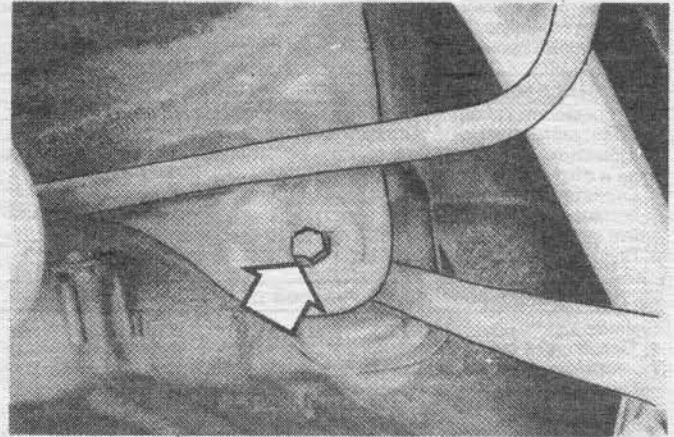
Болт и гайка крепления нижнего рычага к корпусу.
